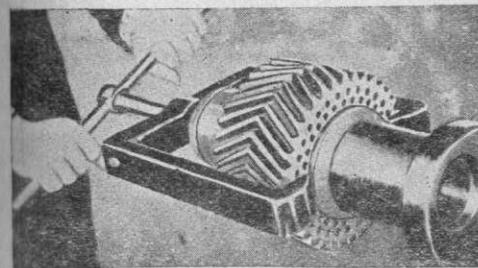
Съемка малой шестерни редуктора с вала мотора АМ-34.
